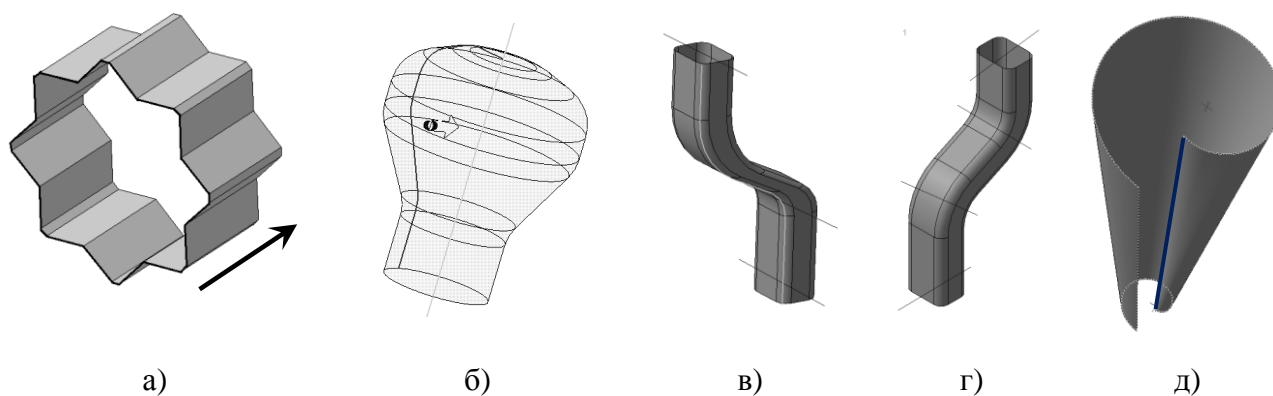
Поверхности движения: а) выдавливания; б) вращения; в) сдвига; г) заметания; д) линейчатая
